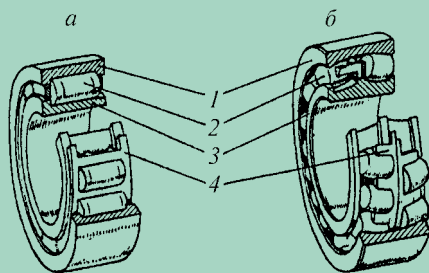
Типы роликовых подшипников: *а* — цилиндрический на горячей посадке; *б* — сферический на втулочной посадке; *1* — наружное кольцо; *2* — ролики; *3* — внутреннее кольцо; *4* — сепаратор
